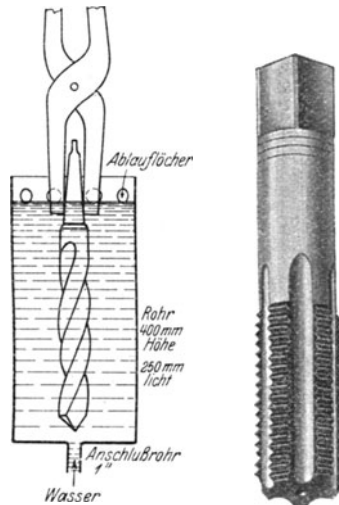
Abkühlen von Spiralbohrern. Fig. 139b. Gewindebohrer.
